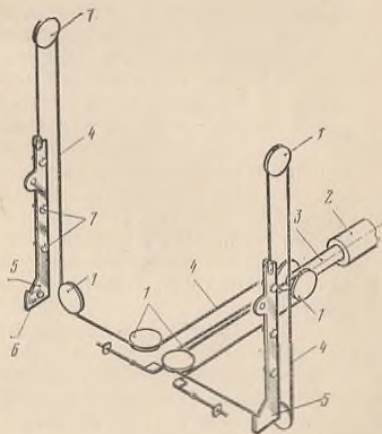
Кинематическая схема подъемного механизма автомобиля У-77:
